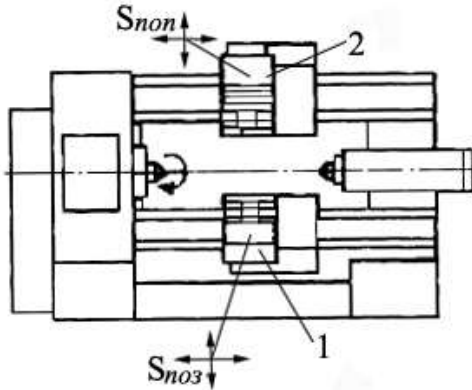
Загальний вигляд токарного багаторізцевого верстата:
